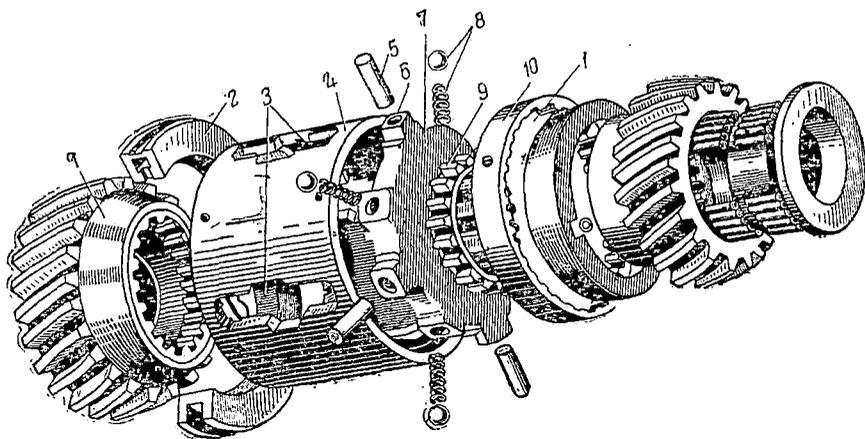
Синхронизатор коробки передач автомобилей МАЗ-200 и КрАЗ-219:
